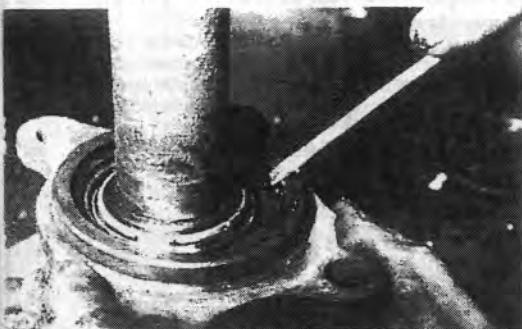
; Dan verschijnt er een klemring (Simmerring). Ook deze voorzichtig verwijderen.
